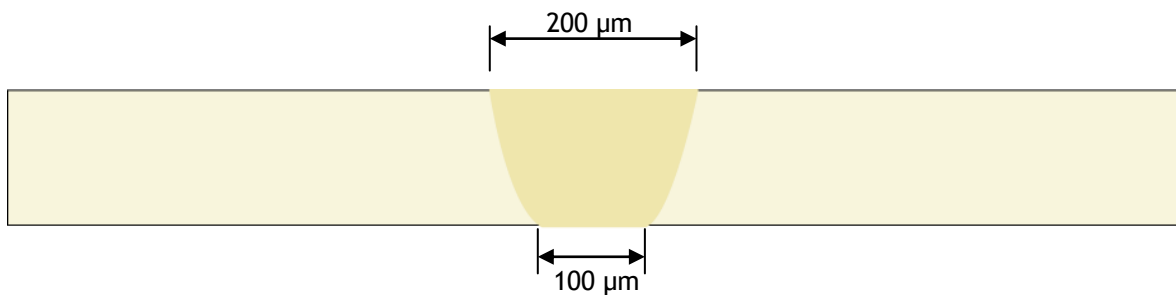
Skizze der gefügten Teil, Schnitt quer zur Schweißnaht
